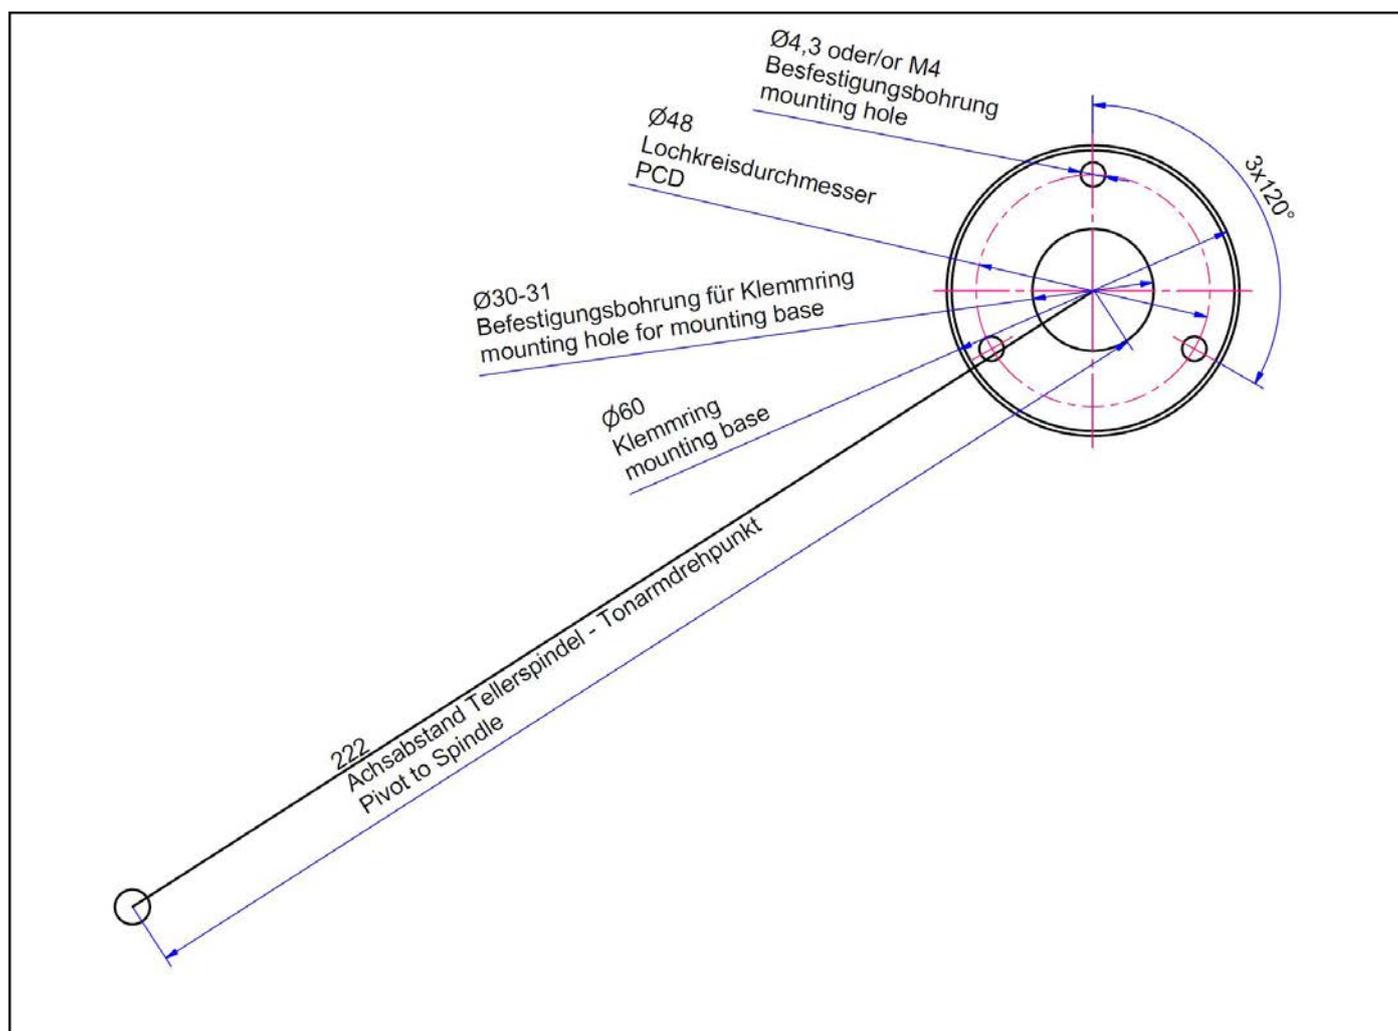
Montage des Klemmrings auf einem Laufwerk anderer Hersteller
